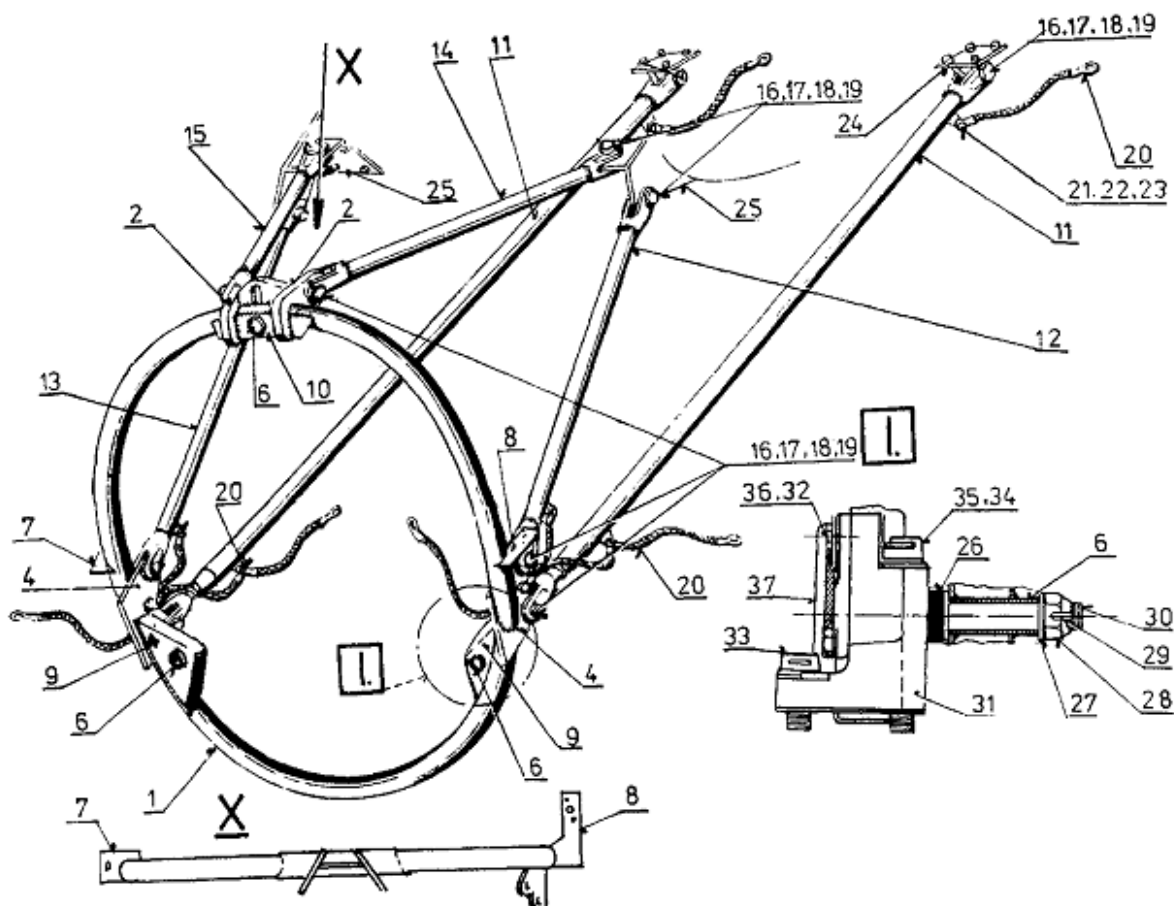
Schéma spojenia závesu motora s motorovými ložmi [40]
